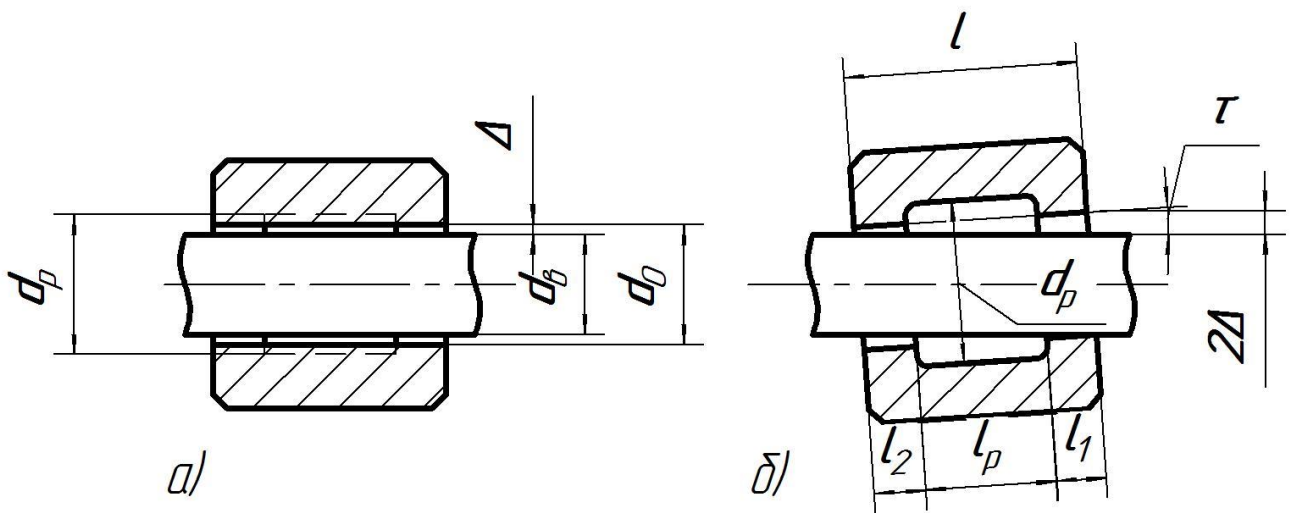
Посадка резца с внутренней расточкой d_p на шейке опорного болта:
